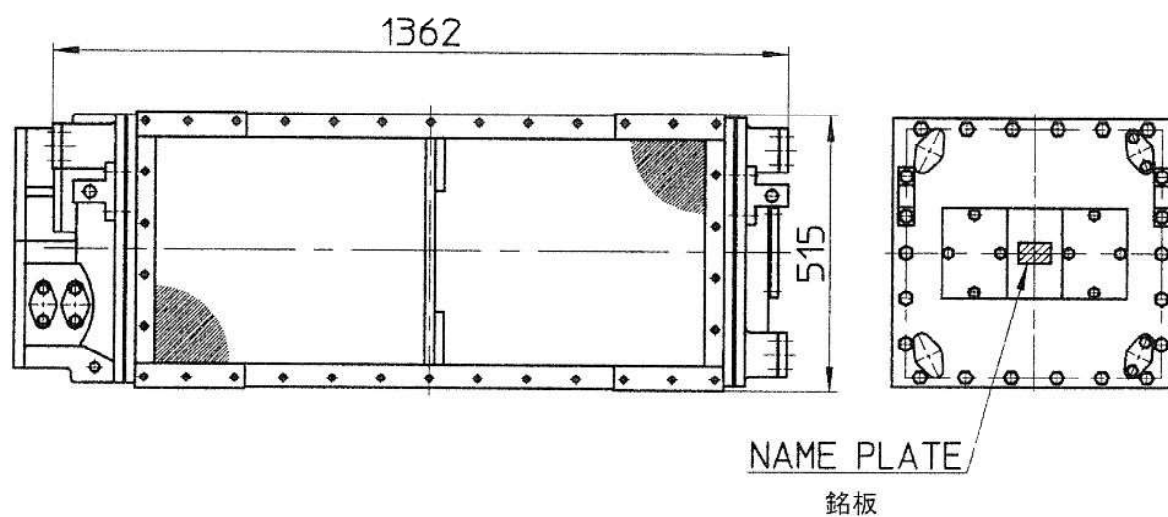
空気冷却器 Air cooler 形式 TYPE ;AHK177S
